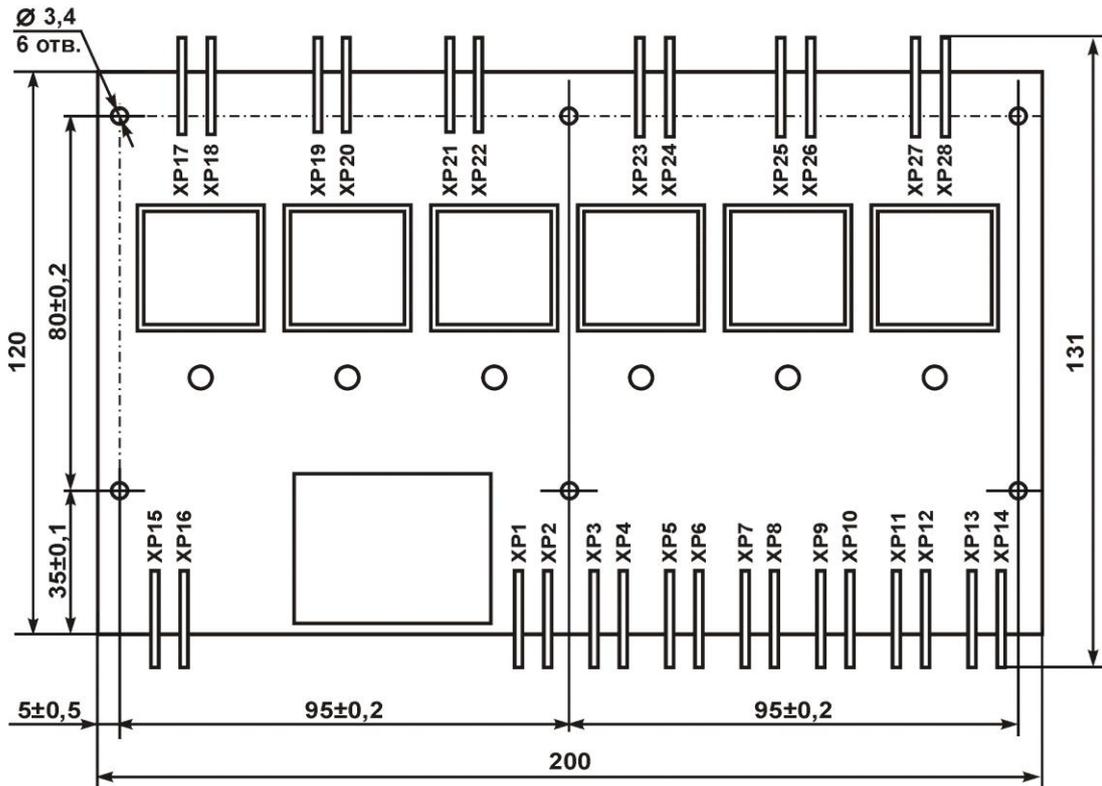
а – Габаритный чертеж ДТ6-Н-Бх
